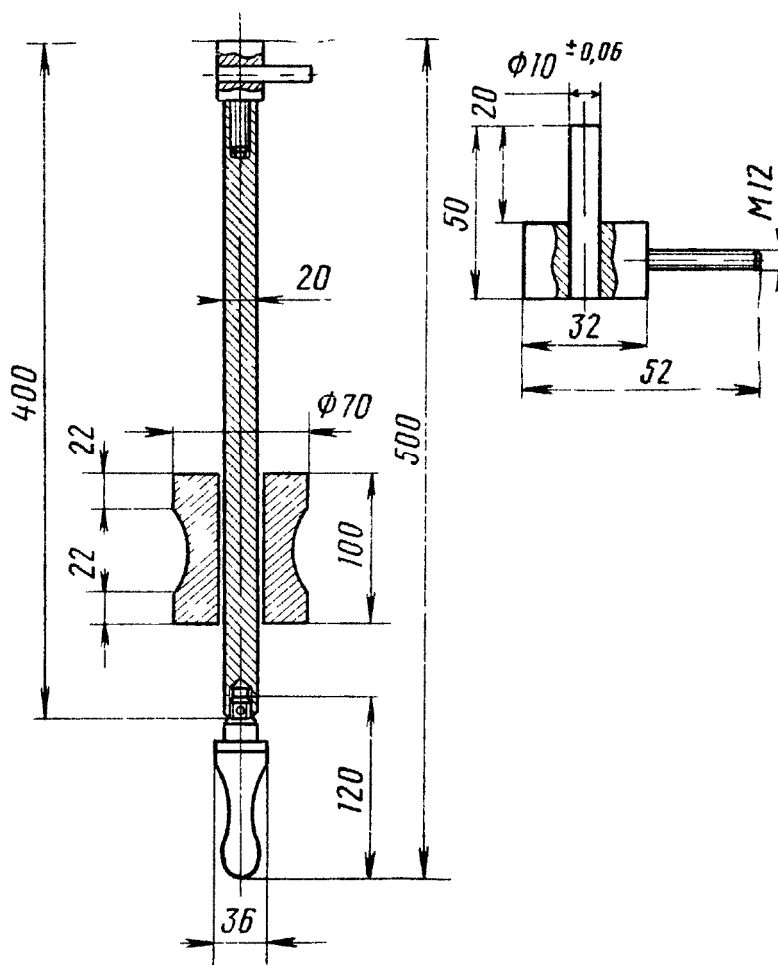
Приспособление для выпрессовки крышек коренных опор коленчатого вала
